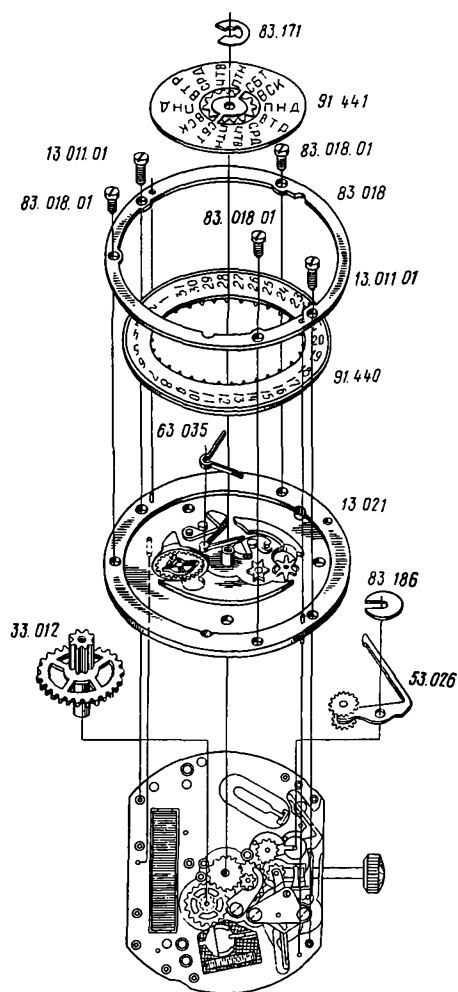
Детали и сборочные единицы календарного устройства механизма часов 2450
